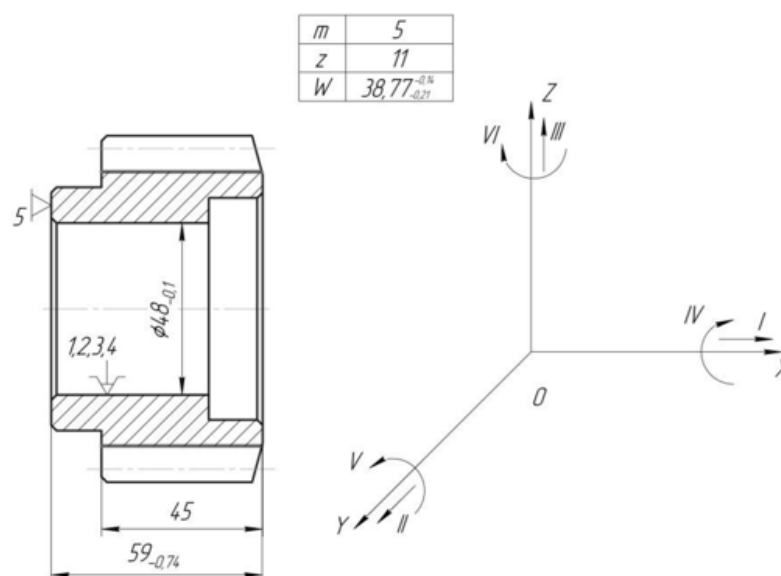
Схема базування для обробки на горизонтально-фрезерному верстаті
